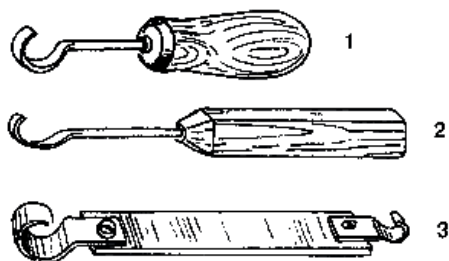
Инструменты: 1 – короткий ложечный резец; 2 – длинный ложечный резец; 3 – двусторонний ложечный резец.
